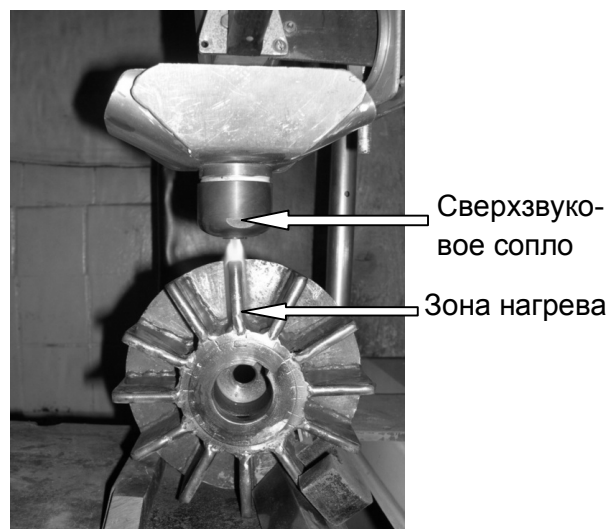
Сверхзвуковая газопорошковая наплавка торцевых и радиальных поверхностей лопастей крыльчатки
